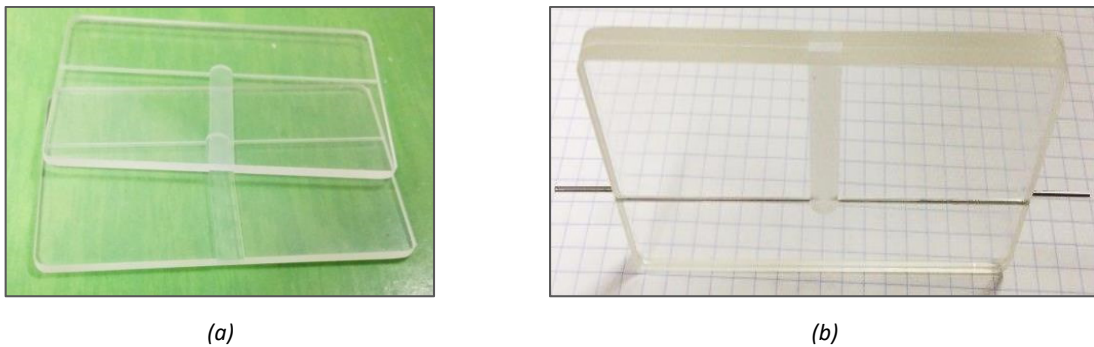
Photographies des cartes : (a) avant assemblage, (b) cuve en U.
